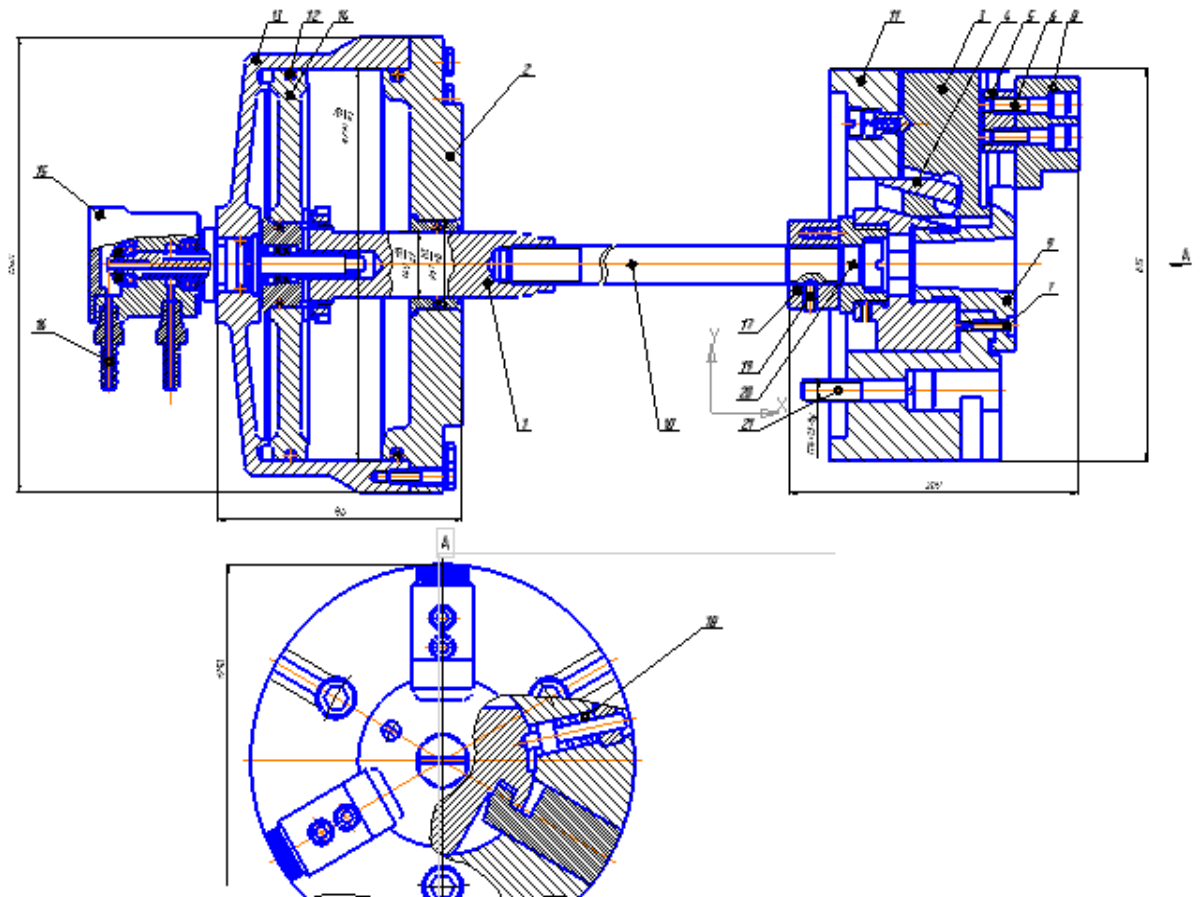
Ескіз 3-х кулачкового патрона
